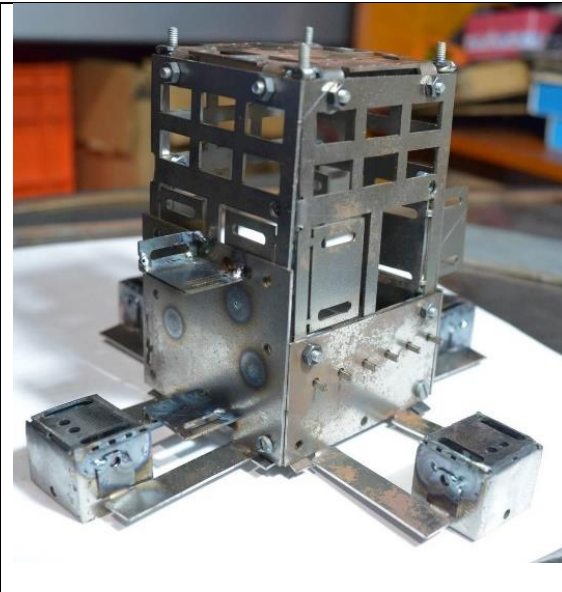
Cuerpo del cabezal (jaula). Corte láser, doblado y soldado con proceso TIG.
